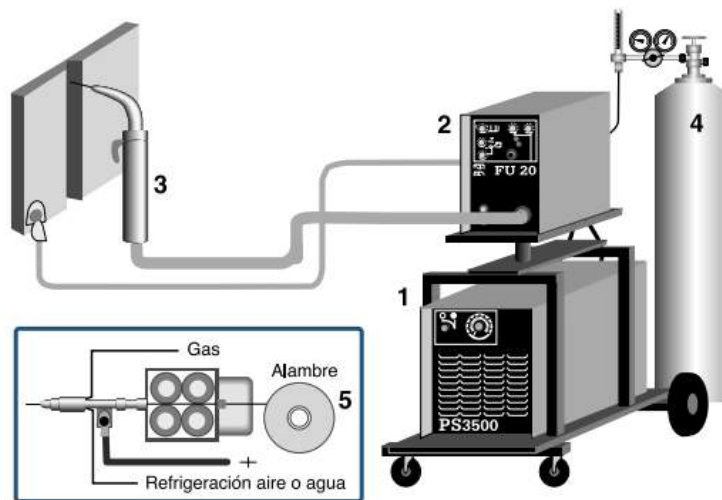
Equipos para soldadura MIG.
